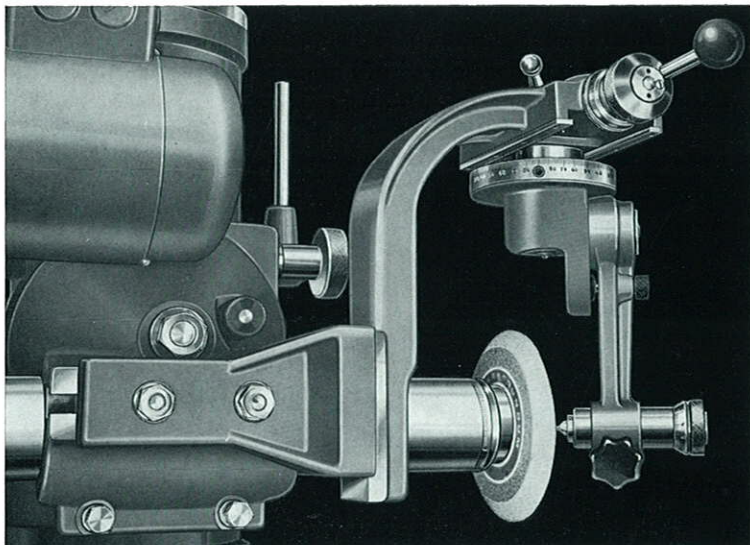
Universal-Abrichtgerät an schwenkbarem Schleifspindelkopf angebaut
